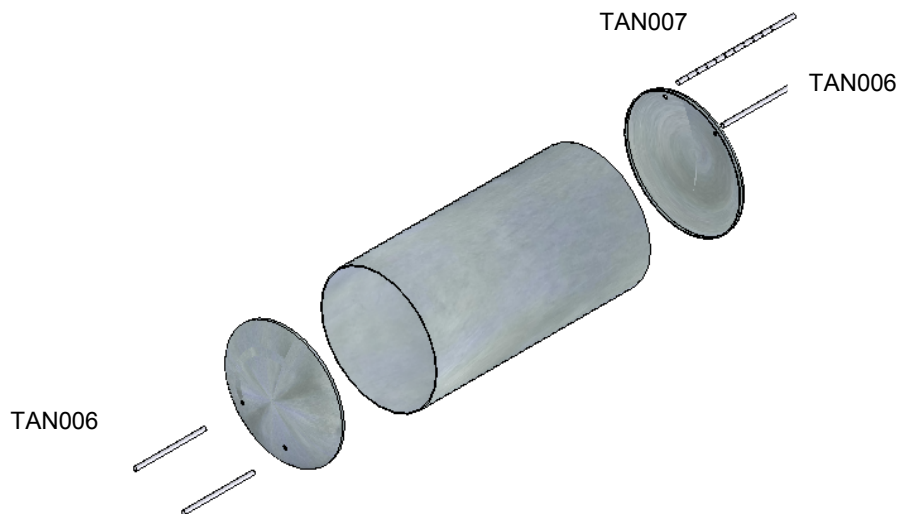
Despiece del Tanque Acumulador y Flautas
